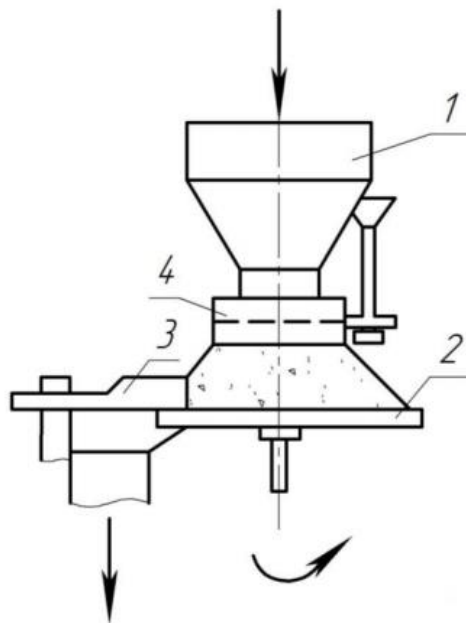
Тарільчастий дозувальний пристрій: 1 – корпус; 2 – тарілка; 3 – шкребок; 4 – патрубок
